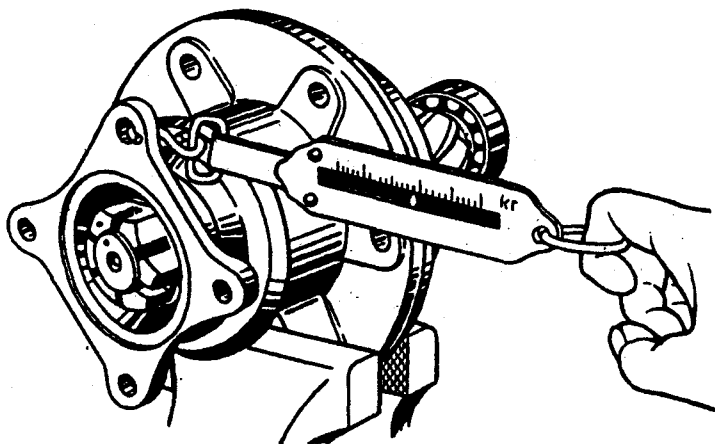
Проверка преднатяга подшипников ведущей шестерни
